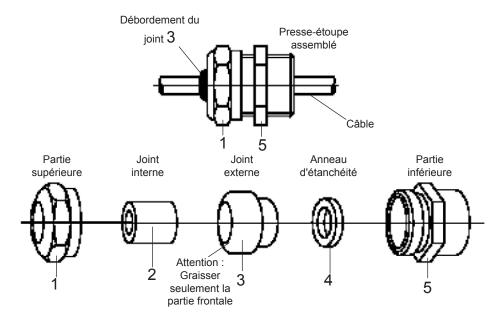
Presse-étoupe (vue d'ensemble et explosée).
